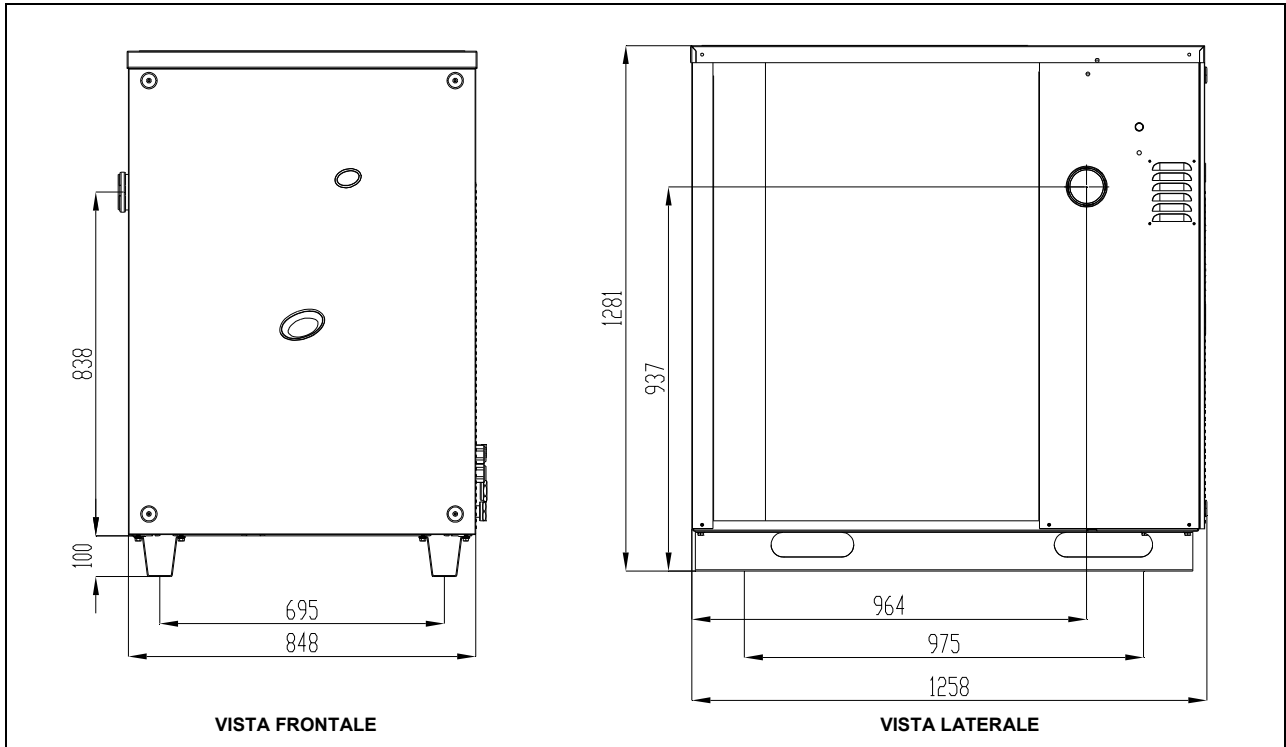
Dimensioni unità GAHP-A - vista frontale e laterale (quote espresse in mm)
